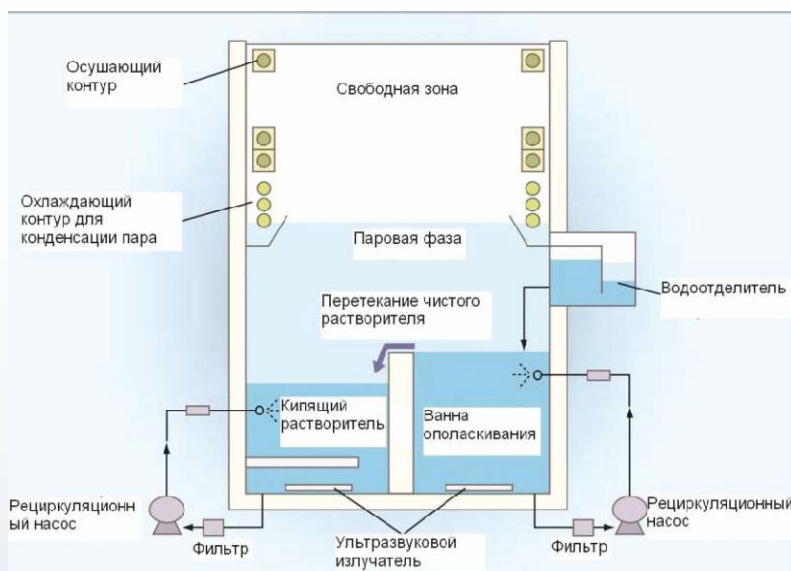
Схема рабочей камеры оборудования для очистки в гидрофторэфирах
